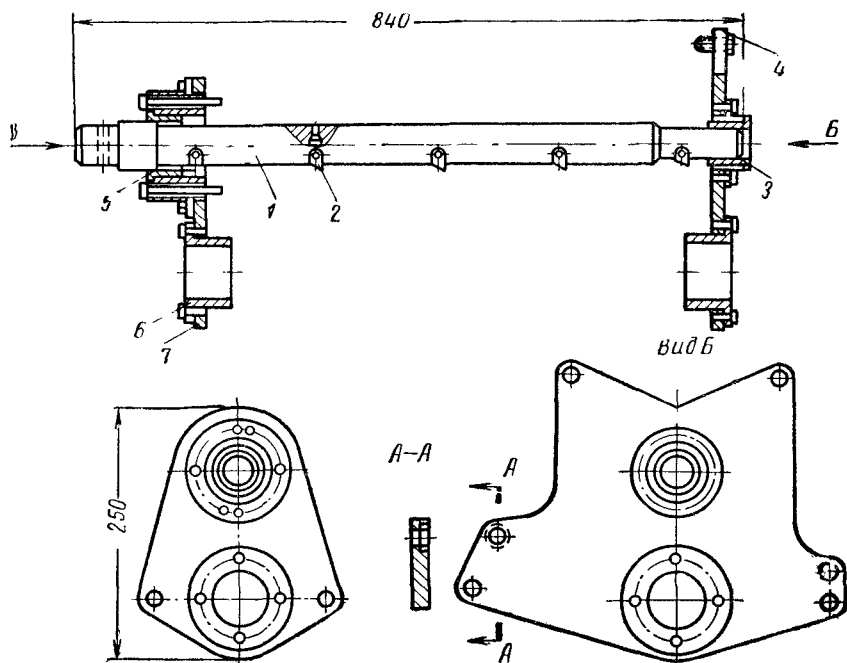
Приспособление для одновременной расточки отверстий в блоке цилиндров ЗИЛ-130
